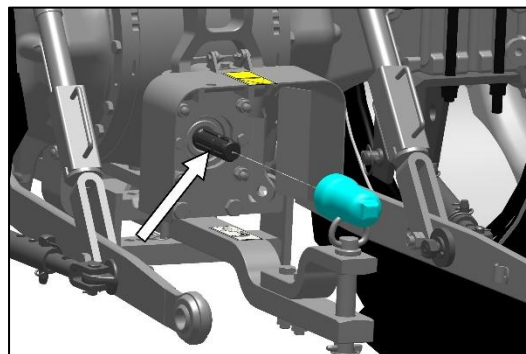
DÉPOSE DU COUVERCLE DE LA PDF
